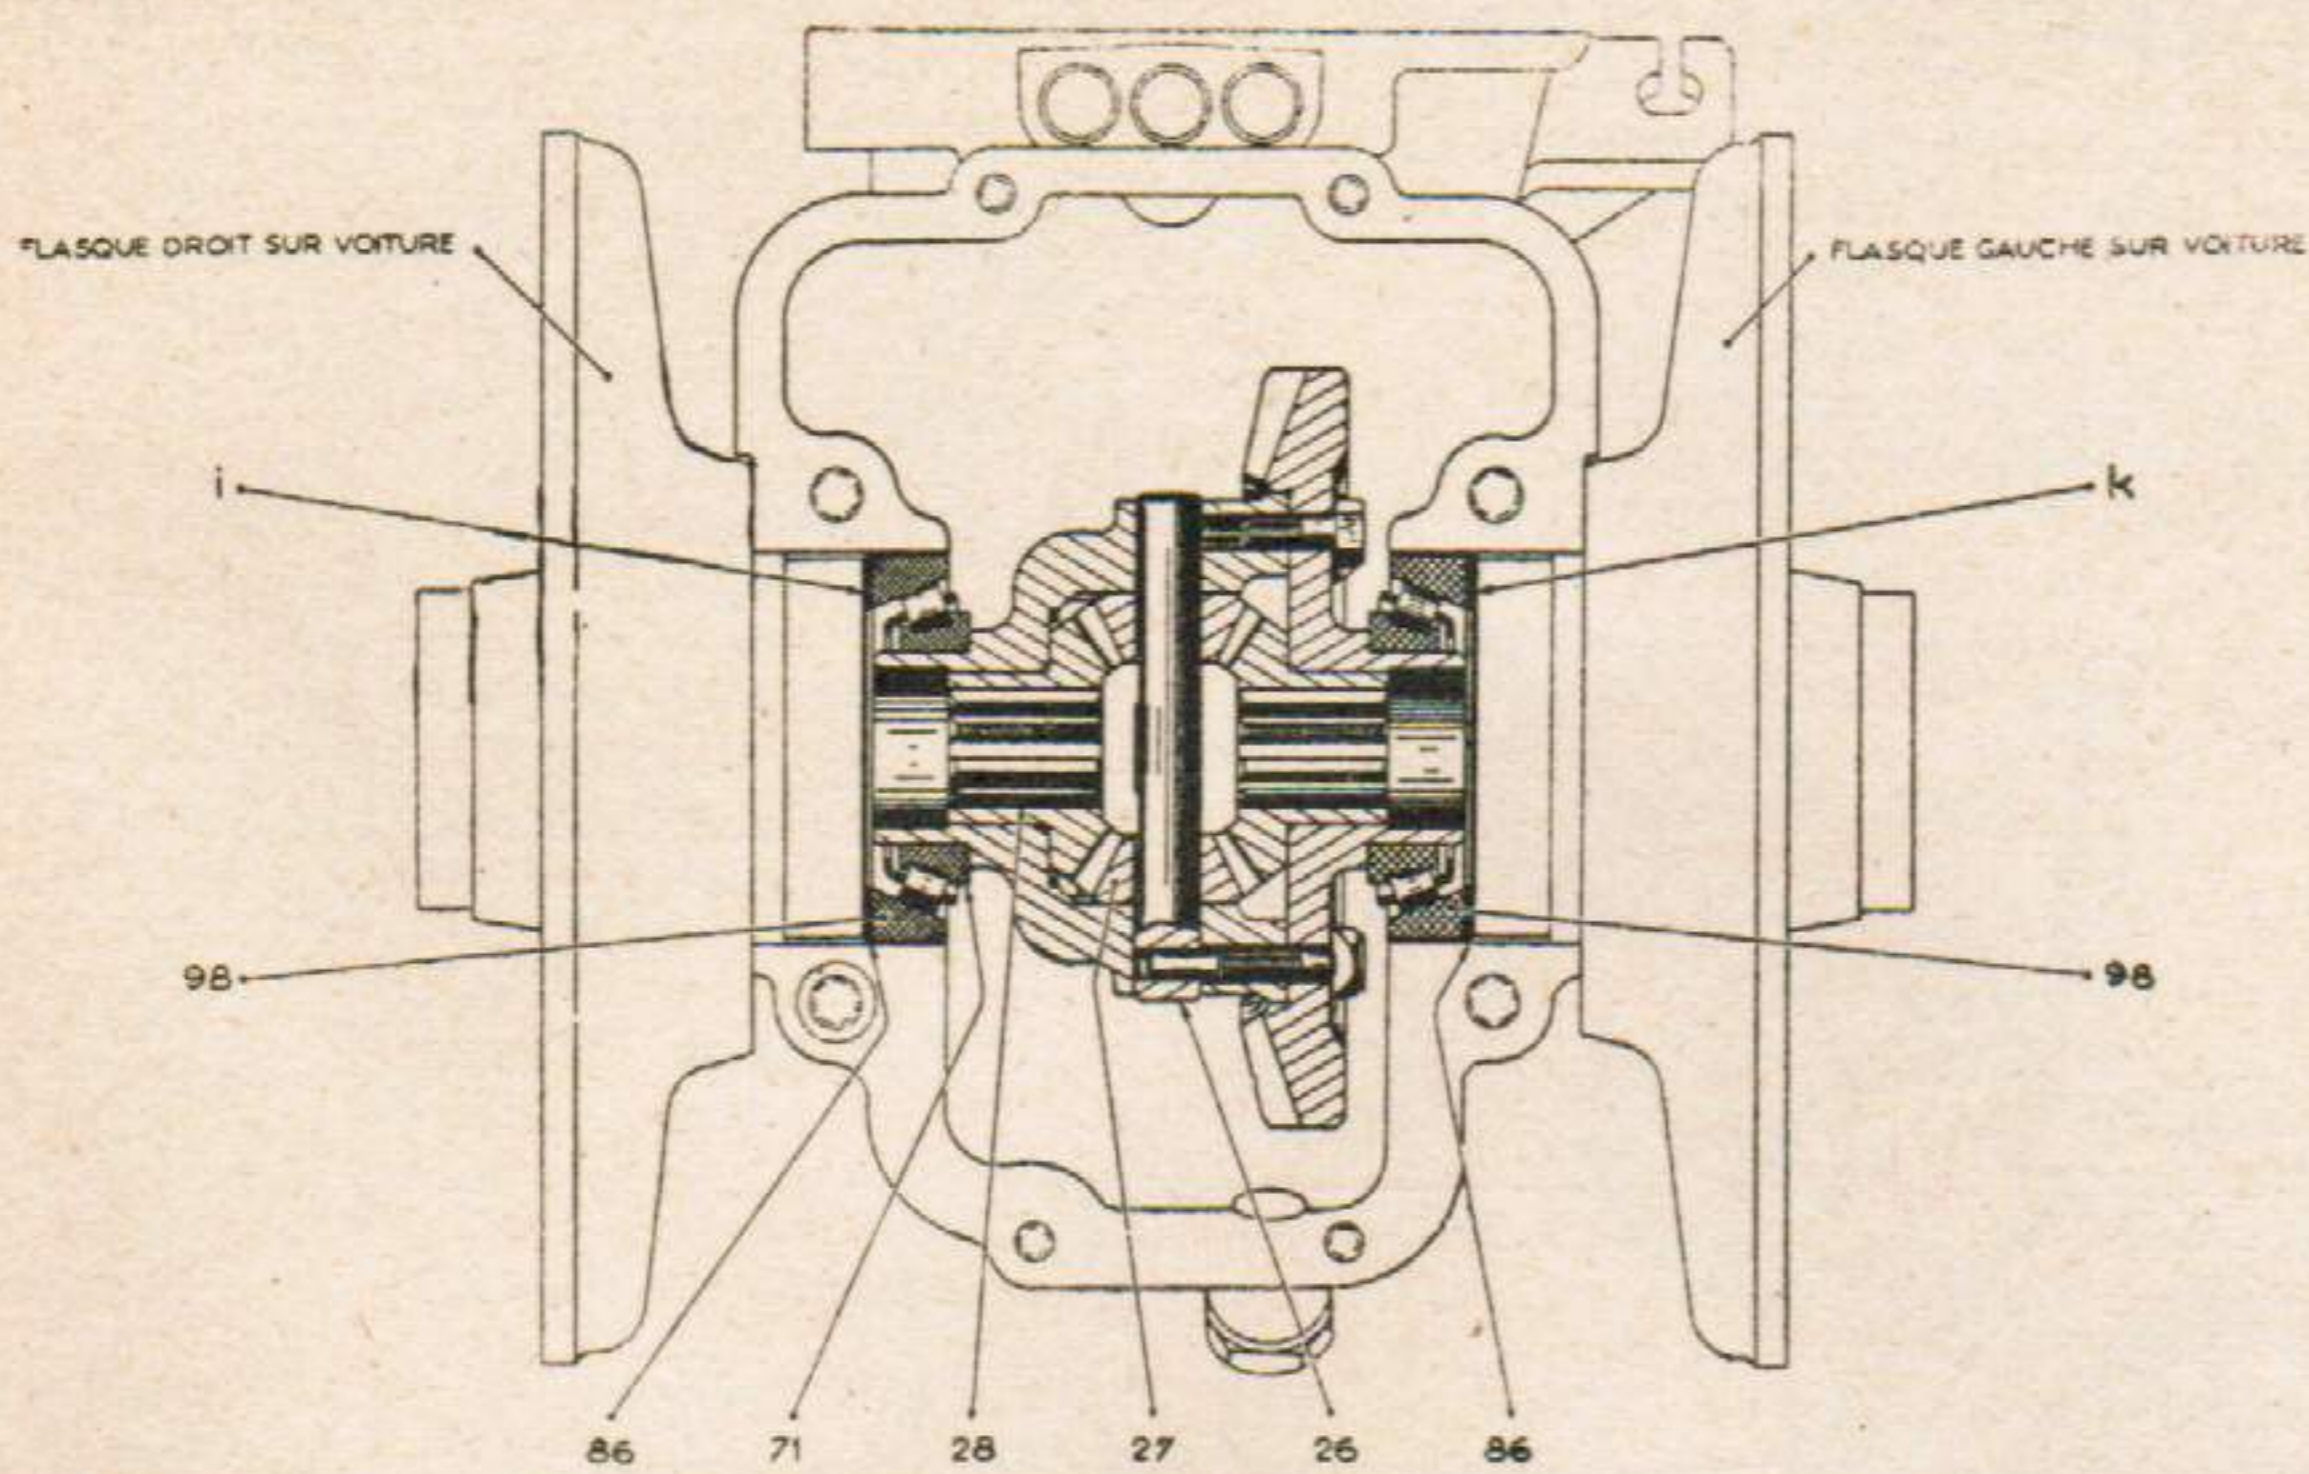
Vue en coupe du différentiel (par l'avant de la voiture)
